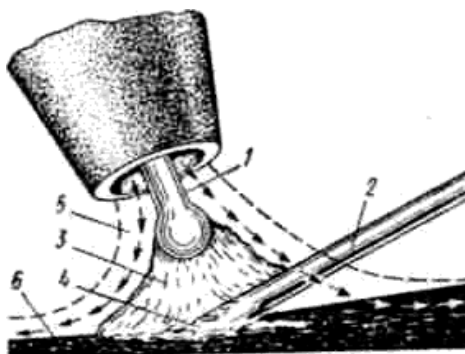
Схема аргоно-дуговой электрической сварки неплавящимся вольфрамовым электродом: 1 — вольфрамовый электрод; 2 — присадочный пруток; 3 — электрическая дуга; 4 — сварочная ванна; 5 — струя газа; 6 — основной металл
